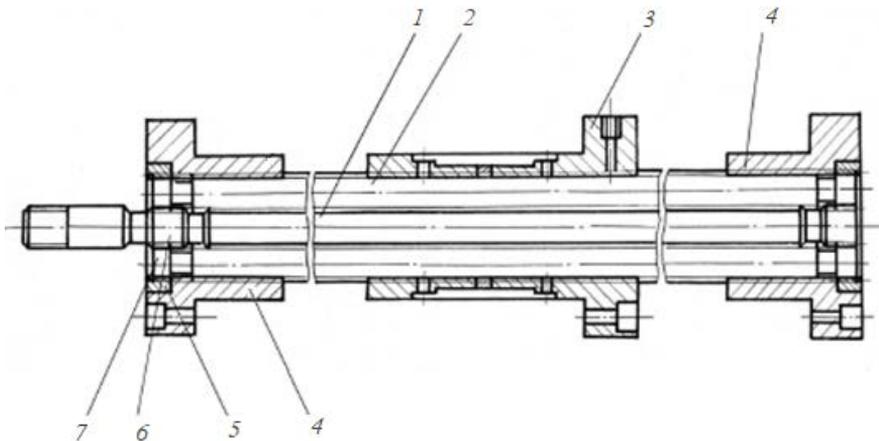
ПРВП с длинными резьбовыми роликами и опорными гайками
